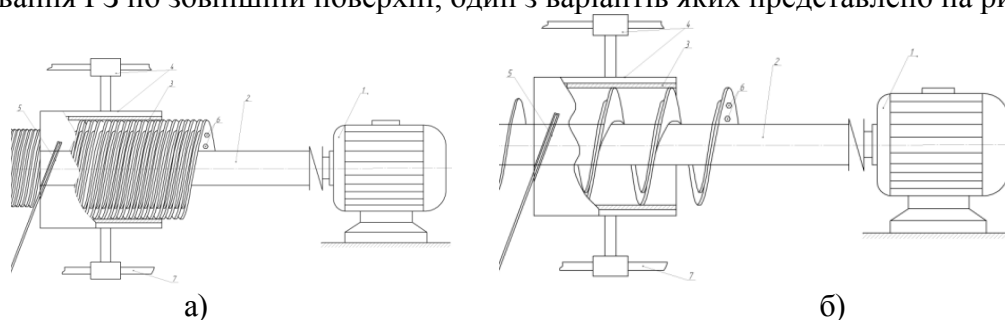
Способи формування гвинтових заготовок по зовнішній поверхні:
